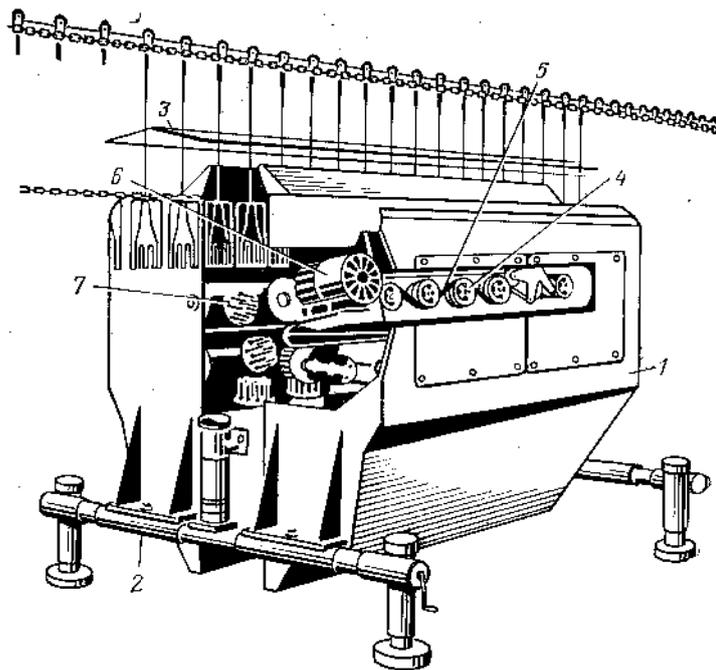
Дисковый автомат для снятия оперения с тушек птицы: 1 – корпус; 2 – опора; 3 – дисковый ряд; 4 – шкив; 5 – клиновой ремень; 6 – подшипниковый узел диска; 7 – перосъемный диск с пальцами; 8 – устройство для подачи воды
